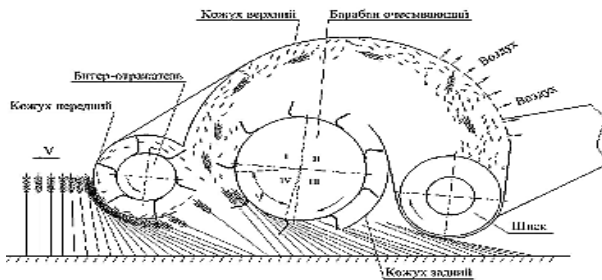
Общий вид двухбарабанной жатки очёсывающего типа «Славянка УАС»
